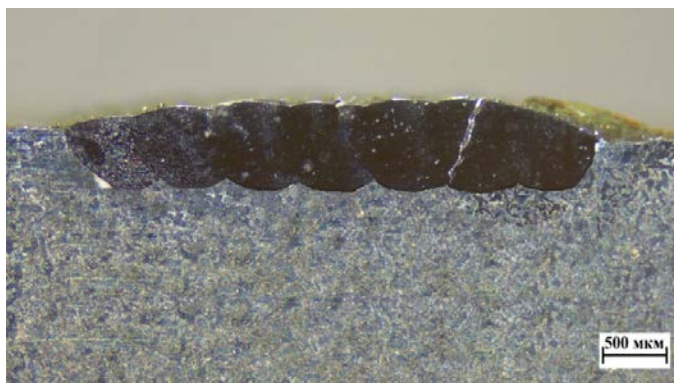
Внешний вид поперечного сечения единичного слоя с шагом наплавки 0,7 мм
